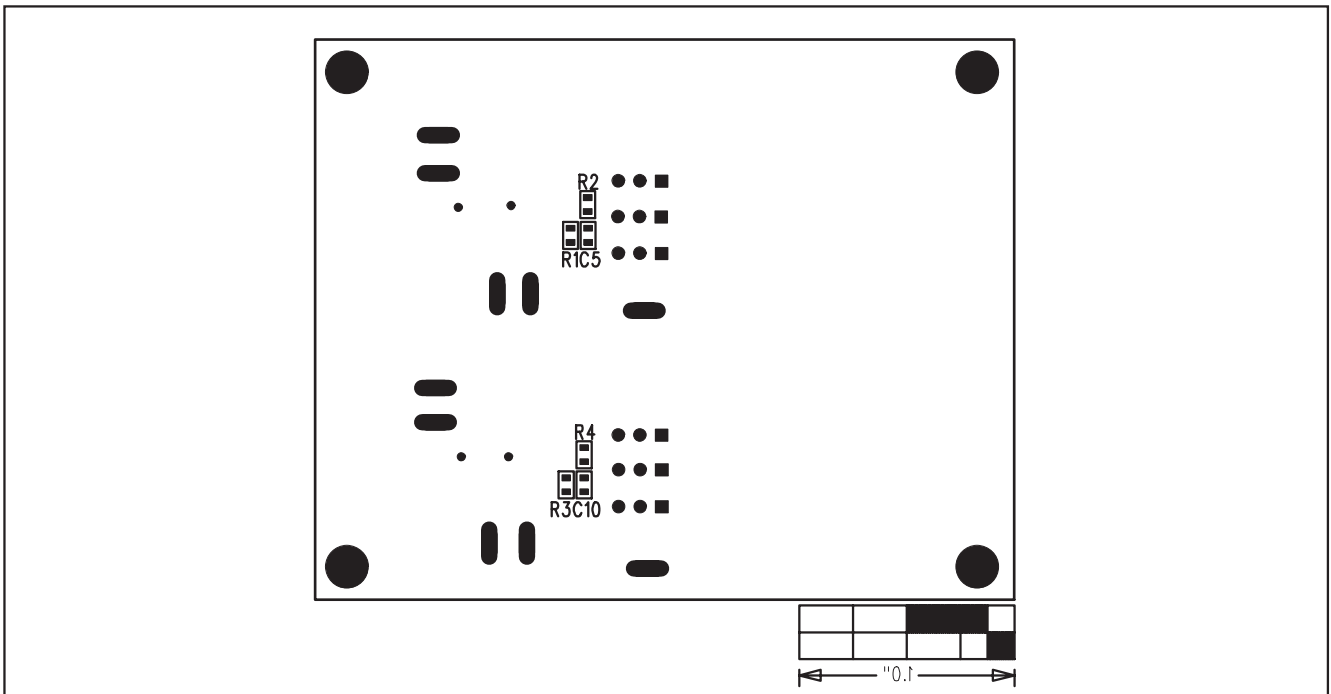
MAX1556 评估板元件布局图 — 焊接面
